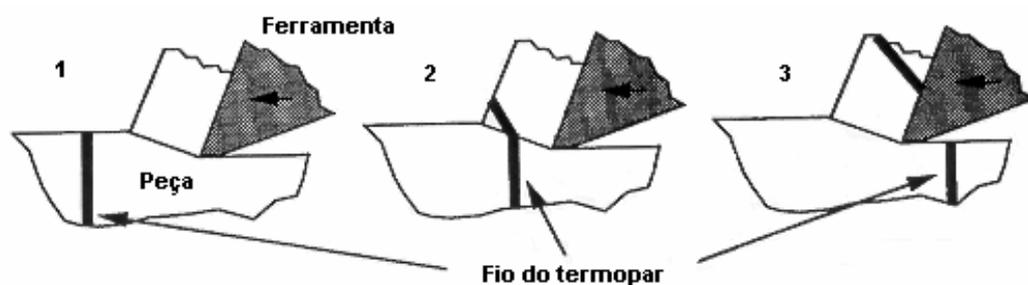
Sequência de usinagem quando se utiliza o termopar implantado na peça.
